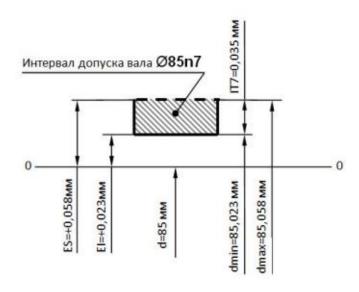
Схема расположения интервала допуска вала Ø85n7
